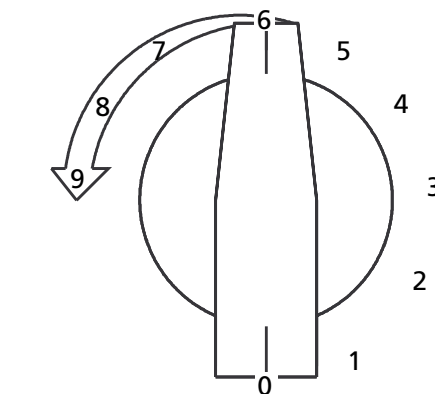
Ajuste de la Presión de Soldadura
